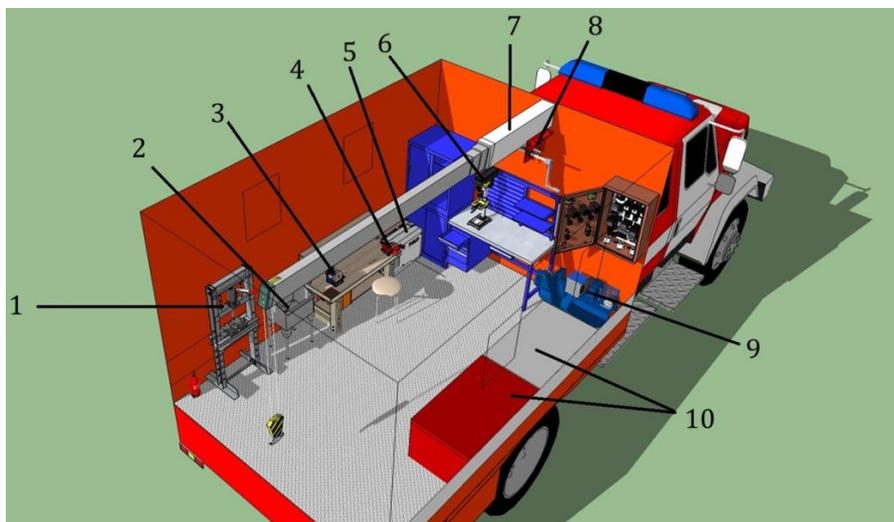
Компоновка полезного объема КУНГа передвижной мастерской: 1 – пресс гидравлический, 2 – мойка, 3 – станок заточной, 4 – тиски, 5 – сварочный аппарат, 6 – сверлильный станок, 7 – грузовая стрела, 8 – редуктор, 9 – компрессор, 10 – рундук
